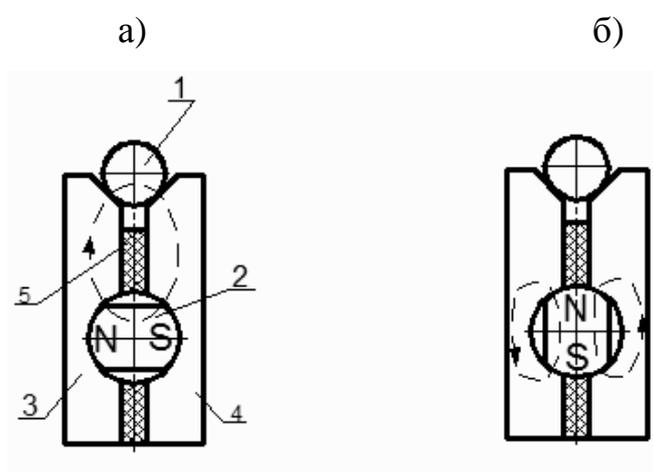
Схема приспособления с постоянным магнитом: а – закреплено,
